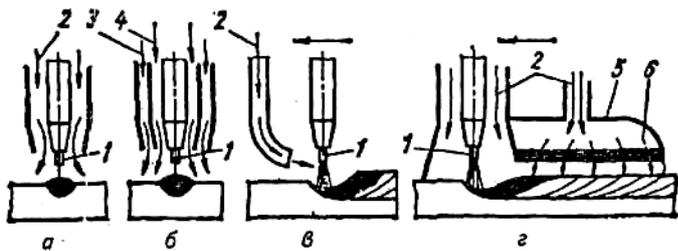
Подача защитных газов в зону сварки: а — центральная одним concentрическим потоком; б — центральная двумя concentрическими потоками; в — боковая; г — в подвижную камеру (насадку); 1 — электрод; 2 — защитный газ; 3, 4 — наружный и внутренний потоки защитных газов; 5 — насадка; 6 — распределительная сетка
